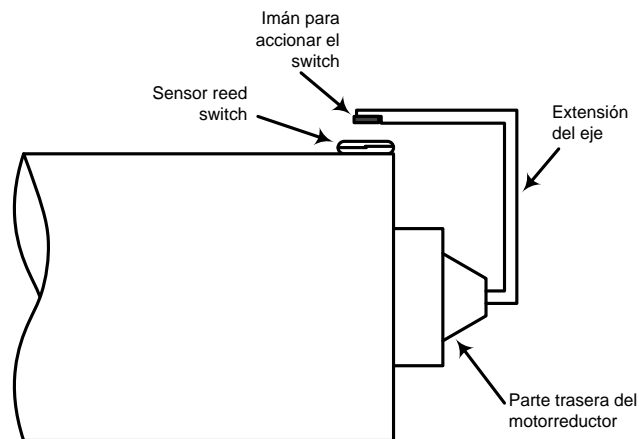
Disposición del sensor reed switch en la parte trasera del motorreductor.
